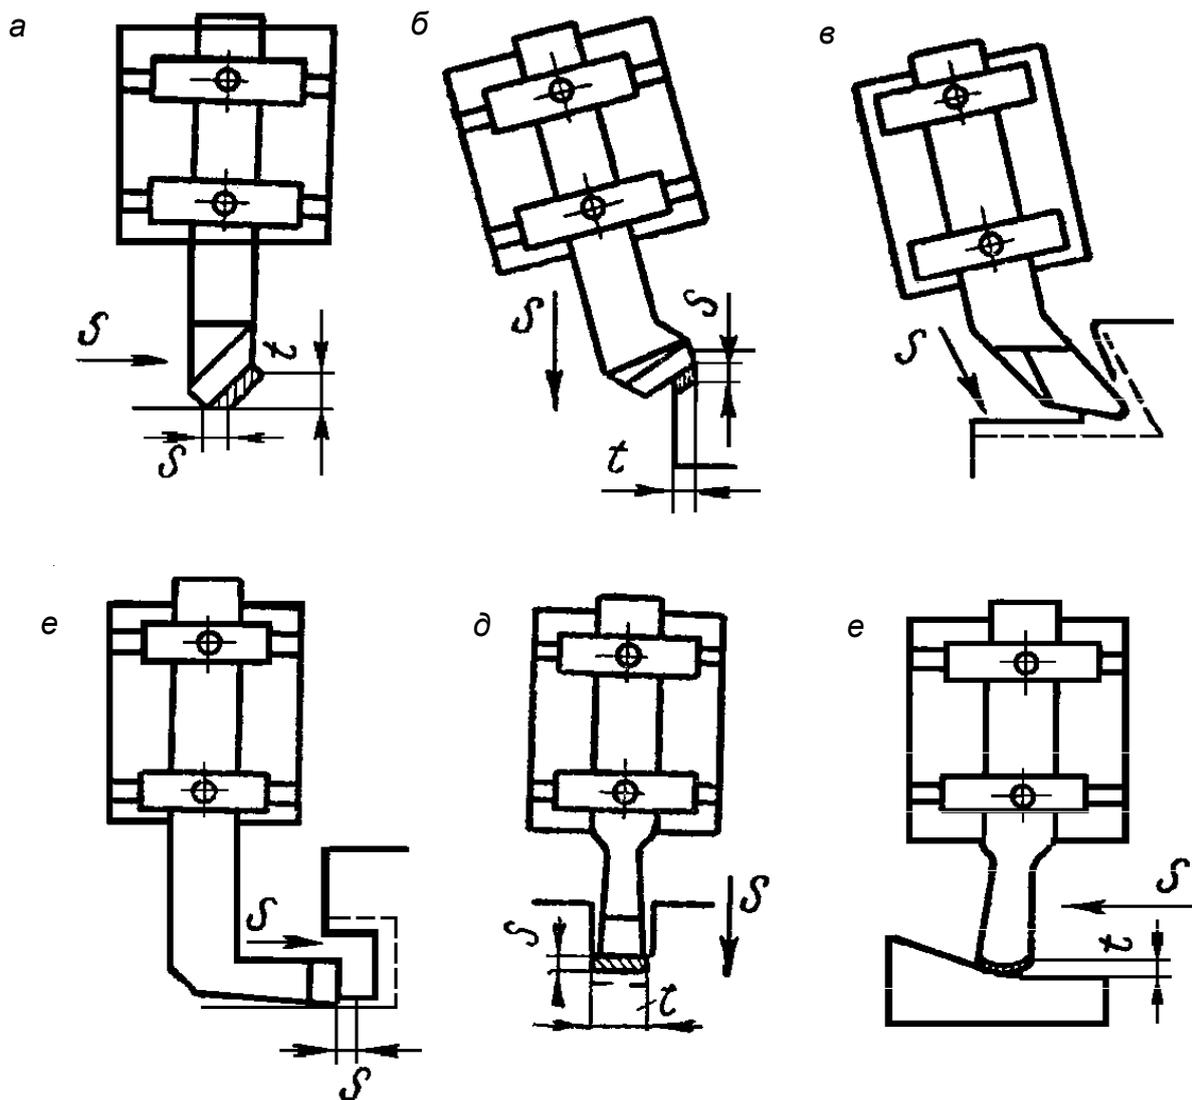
Основные виды плоских и фасонных поверхностей пазов и канавок, обрабатываемых строганием: а – черновое строгание; б – обработка вертикальных плоскостей подрезными и проходными резцами; в – обработка наклонных поверхностей подрезными и проходными резцами специальных форм; г – строгание пазов изогнутыми резцами; д – строгание канавок прямыми резцами; е – обработка фасонных поверхностей
